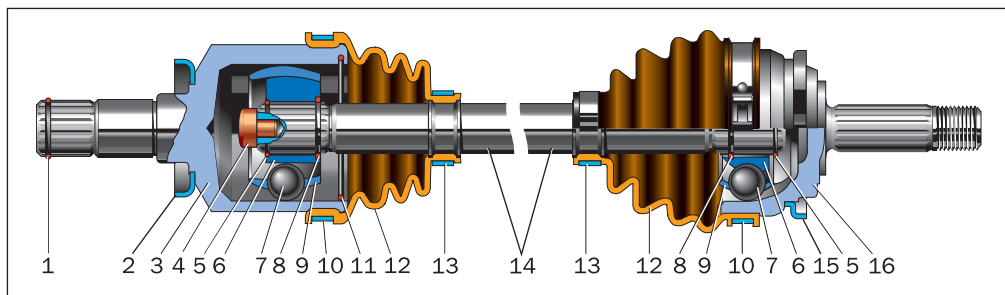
Шестишариковые шарниры равных угловых скоростей: 1 — стопорное кольцо корпуса внутреннего шарнира; 2 — защитное кольцо внутреннего шарнира; 3 — корпус внутреннего шарнира; 4 — упор вала; 5 — стопорное кольцо; 6 — обойма; 7 — шарик; 8 — упорное кольцо; 9 — сепаратор; 10 — наружный хомут; 11 — фиксатор внутреннего шарнира; 12 — защитный чехол; 13 — внутренний хомут; 14 — вал привода колеса; 15 — защитное кольцо наружного шарнира; 16 — корпус наружного шарнира
